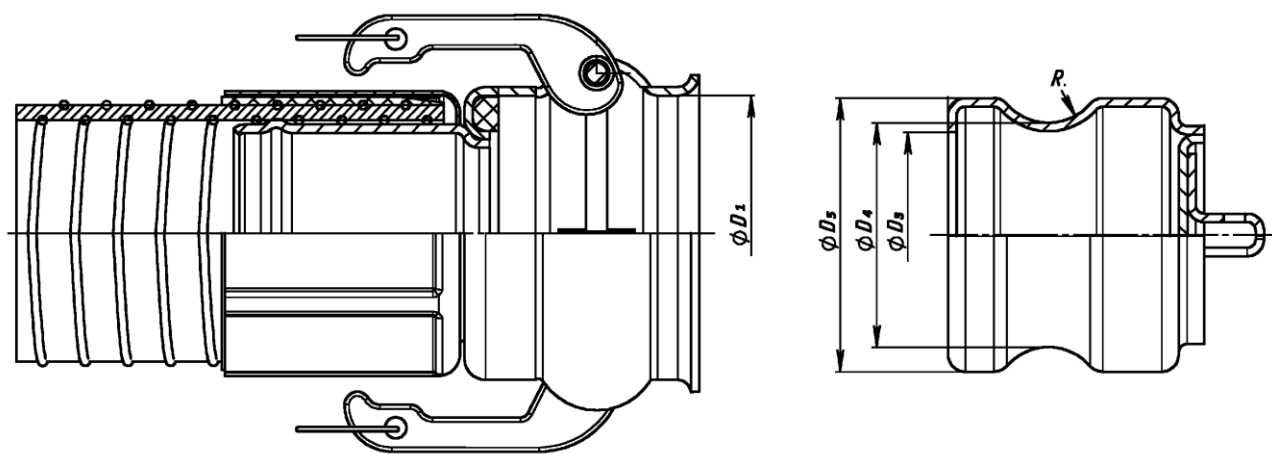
Пристыковочные и присоединительные размеры головок присоединительных с кулачковой муфтой:
